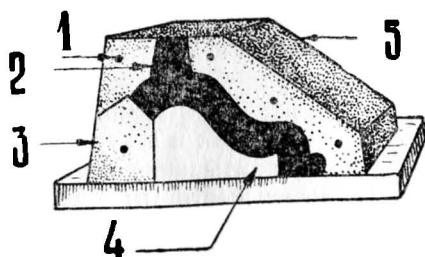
Поперечный разрез наполненной клеем формы: 1 — арматура, 2 — клеевая форма, 3 — задний кусок, 4 — модель каблучка, 5 — кожа
